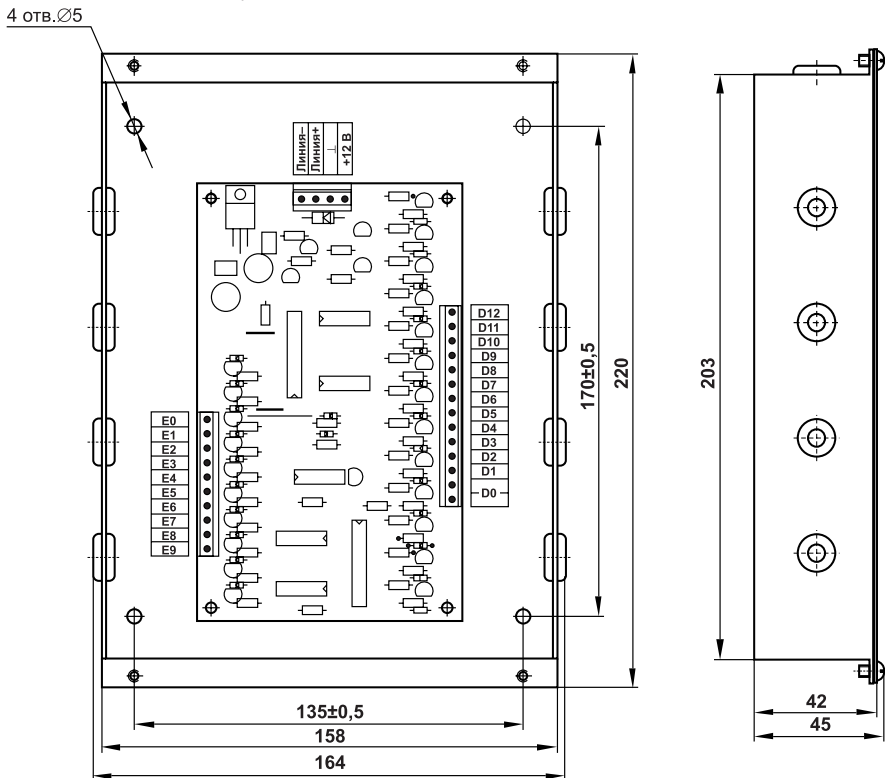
Габаритный чертеж коммутатора PERCo-C-128
